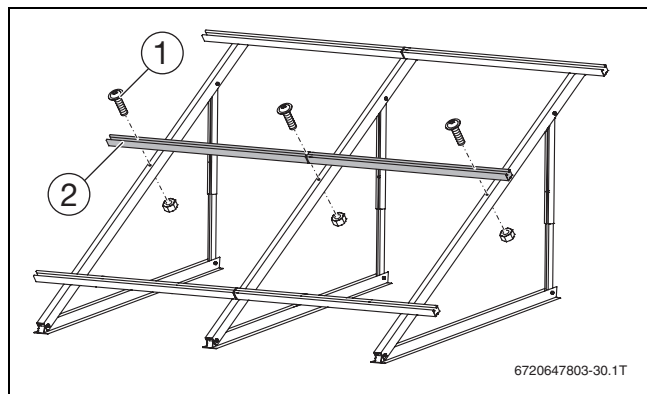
Montaggio di guide profilate aggiuntive (qui: 2 collettori verticali)
